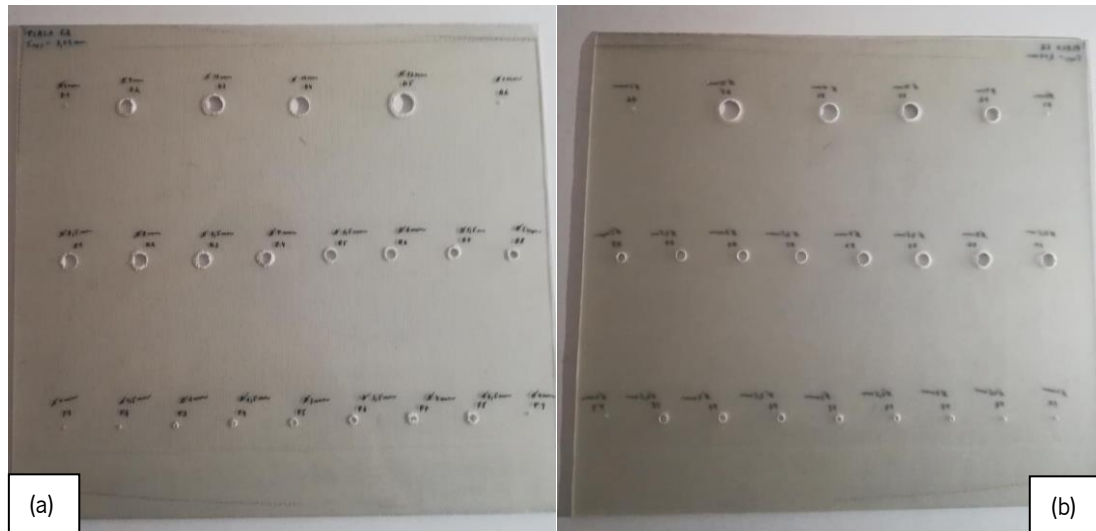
Laminado F_2 com furos passantes de diâmetros distintos – (a) face frontal da placa; (b) face oposta da placa.
